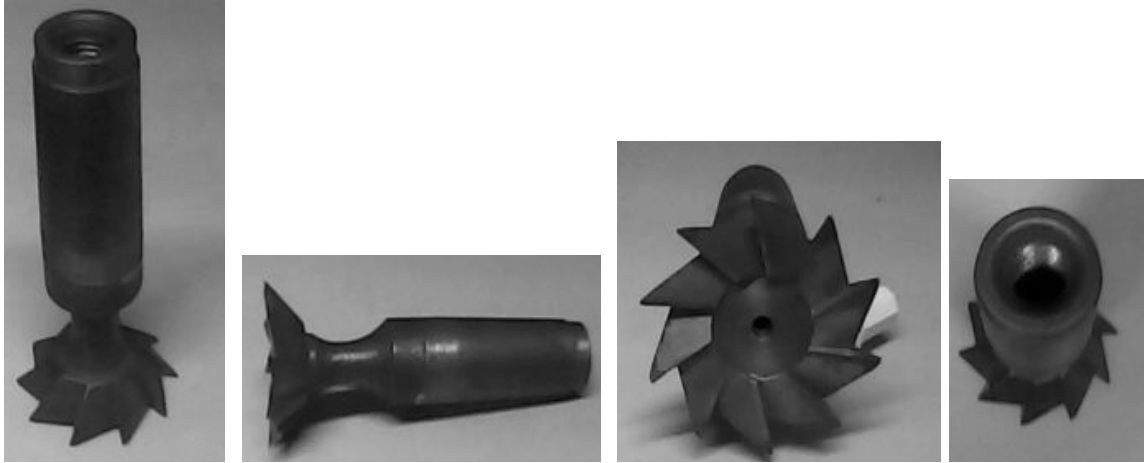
Vistas de la fresa angular de vástago fabricada.
